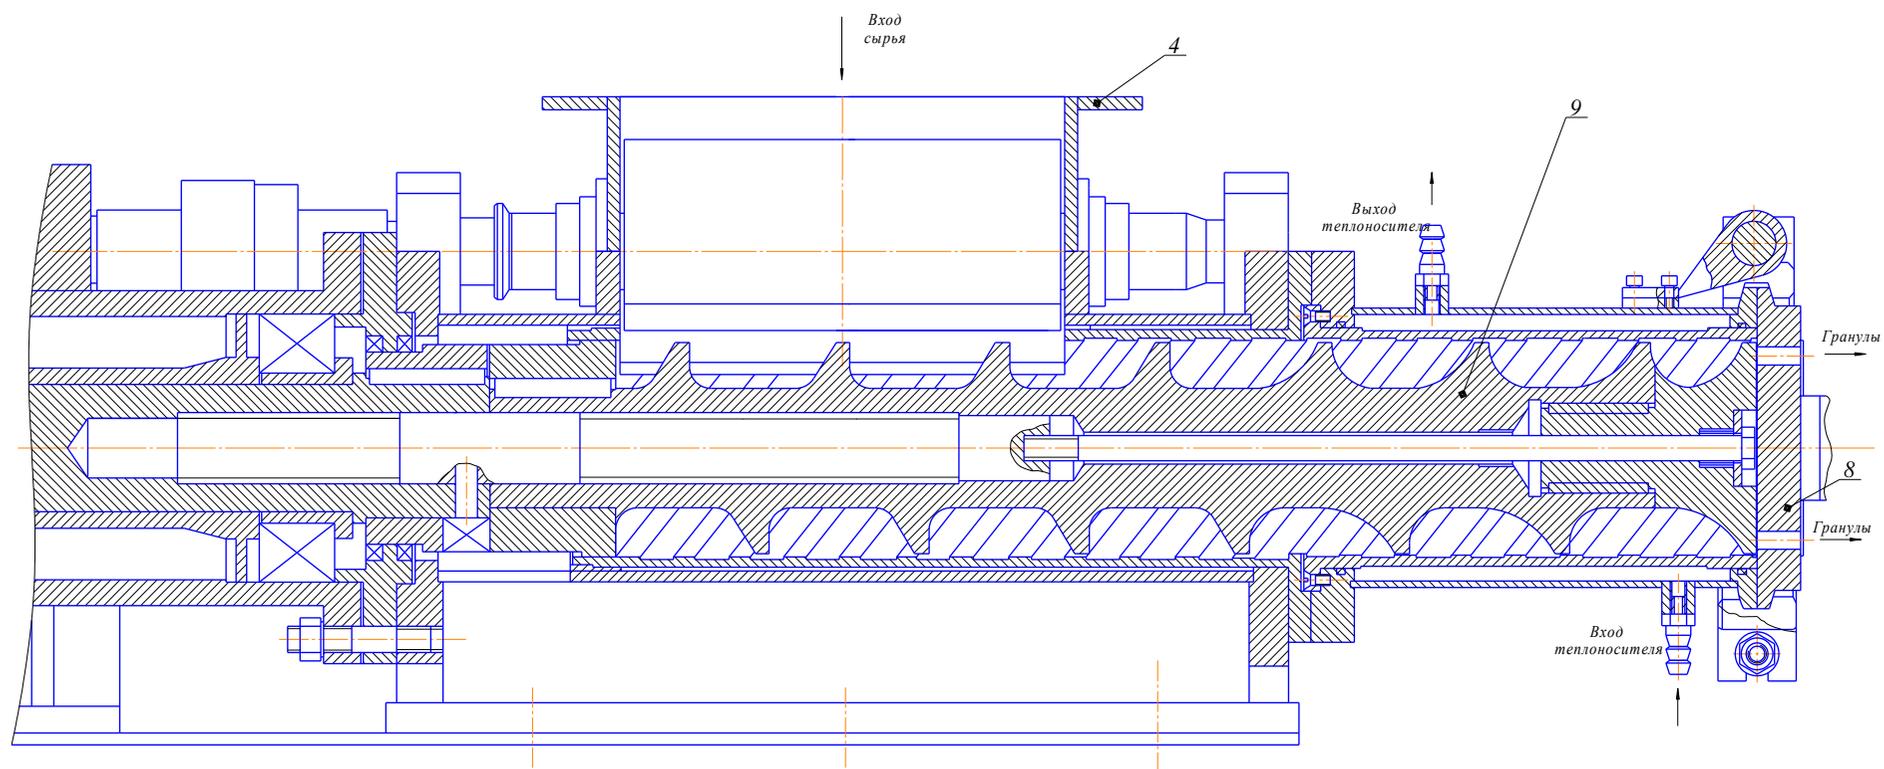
Рабочая камера: 4 – загрузочная камера; 8 – фильера; 9 – шнек
